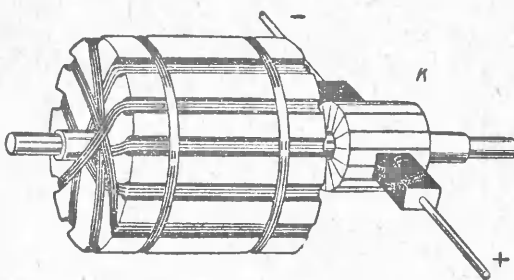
Якорь двигателя постоянного тока с пластинчатым коллектором.
